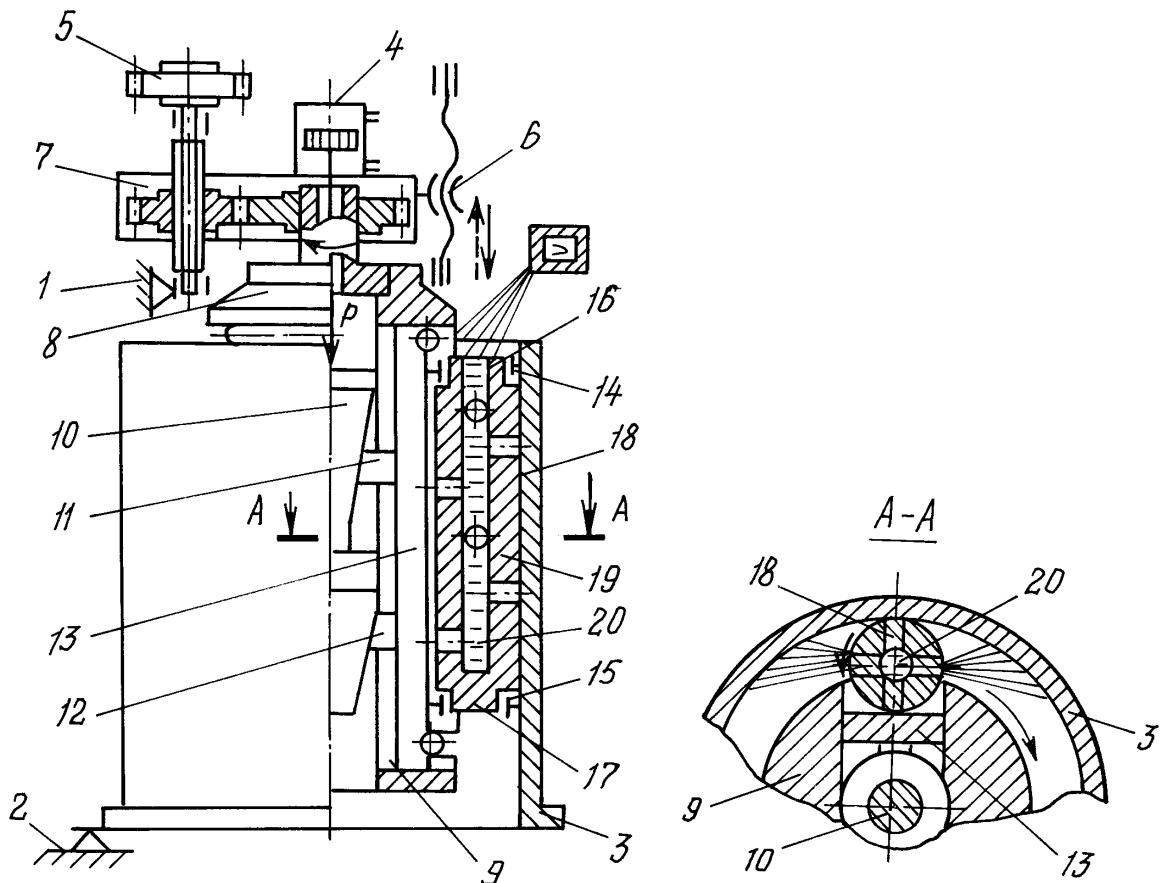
Загальний вигляд схеми способу прецизійного латунювання гільз циліндрів та деталей типу втулка
